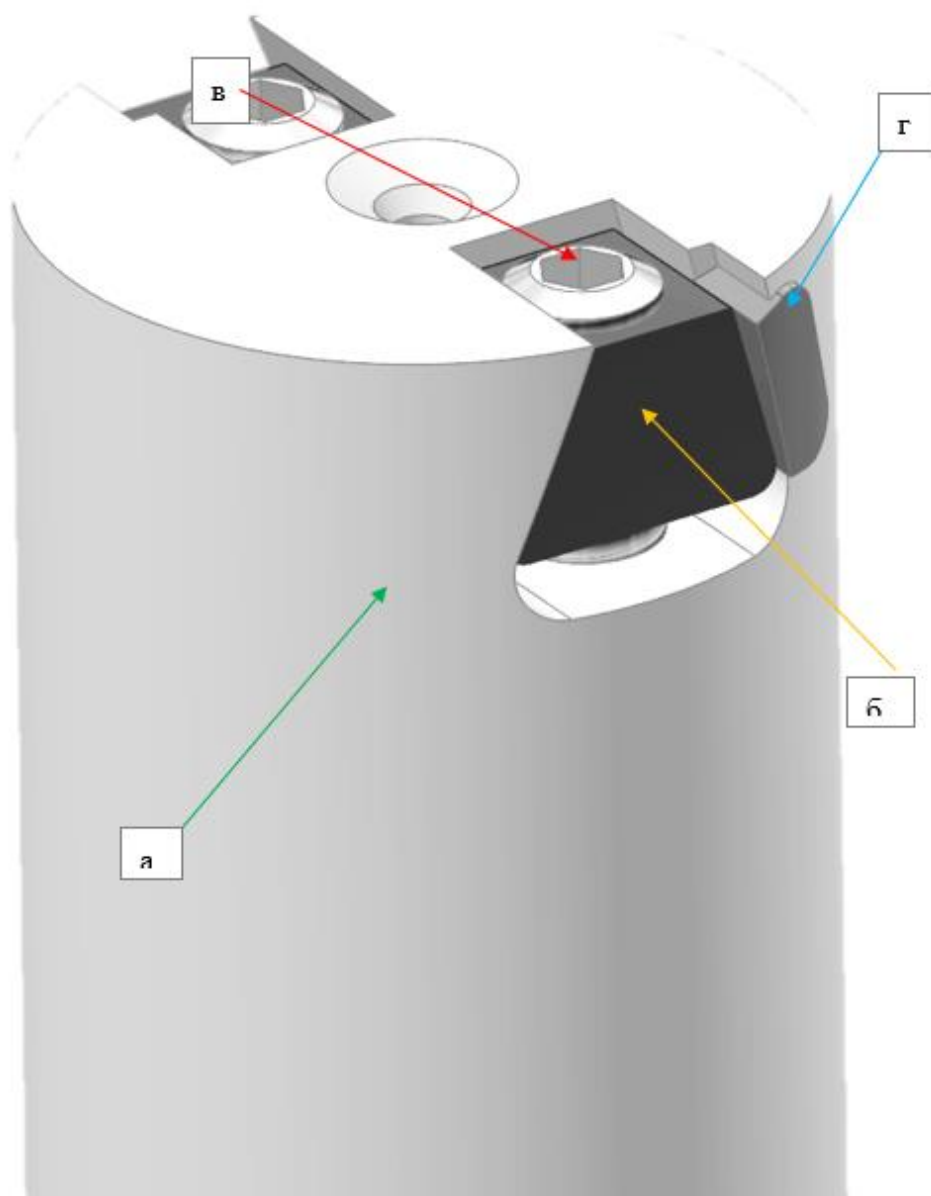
Конструкція пристосування: (а - корпус пристосування, б – клин, в – гвинт, г - АТП)
